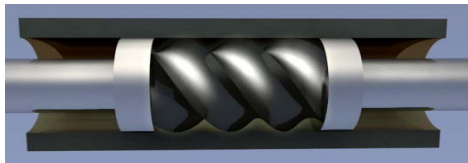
Установка скрученной заготовки в круглый штамп с последующим прессованием
